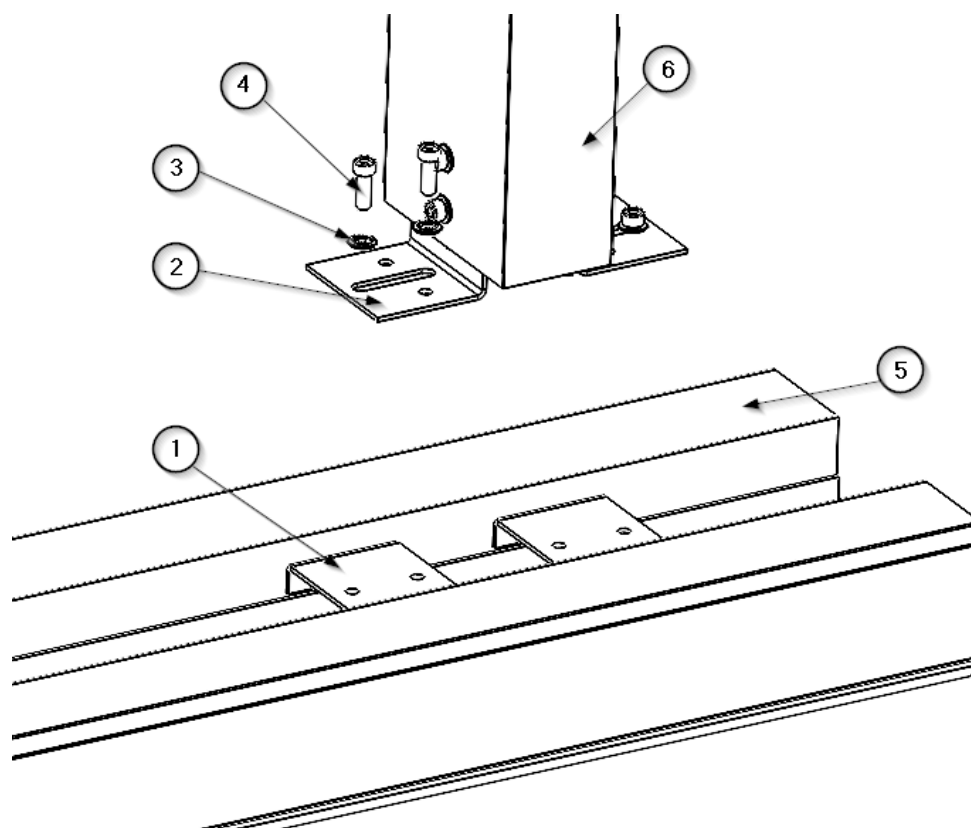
Schéma d'ancrage d'une section du corps principal de l'ATLAS sur un tuyau de descente
